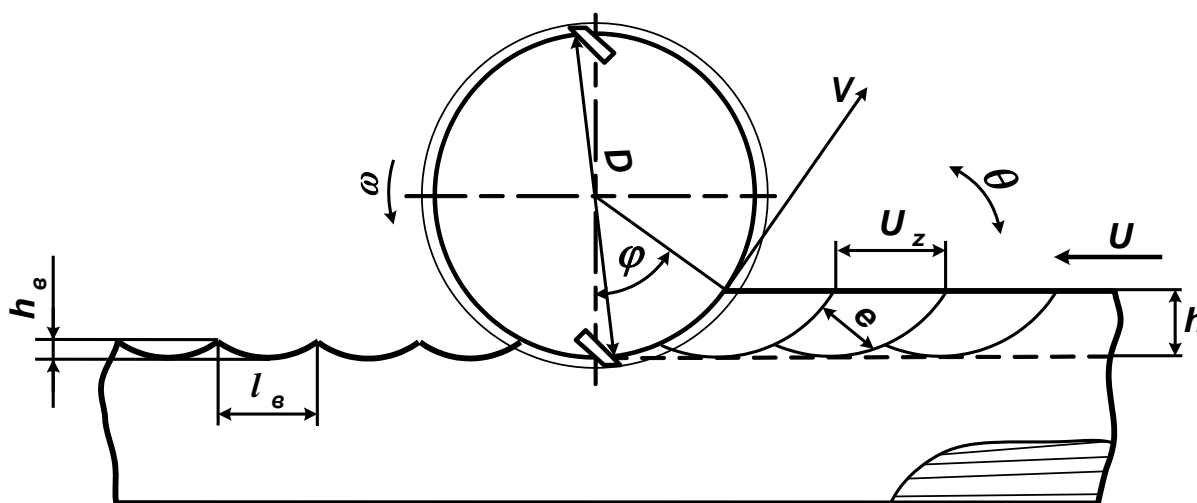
Схема продольно-торцевого цилиндрического фрезерования
